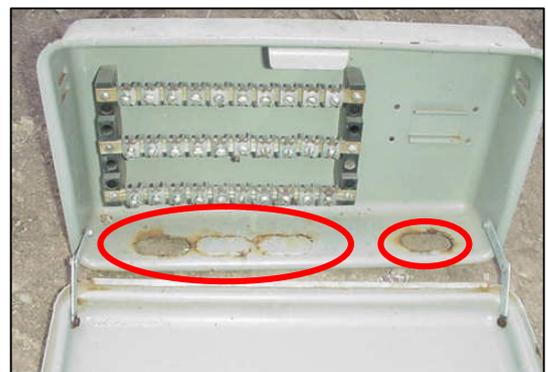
Corrosión en troqueles u orificios para cables.
